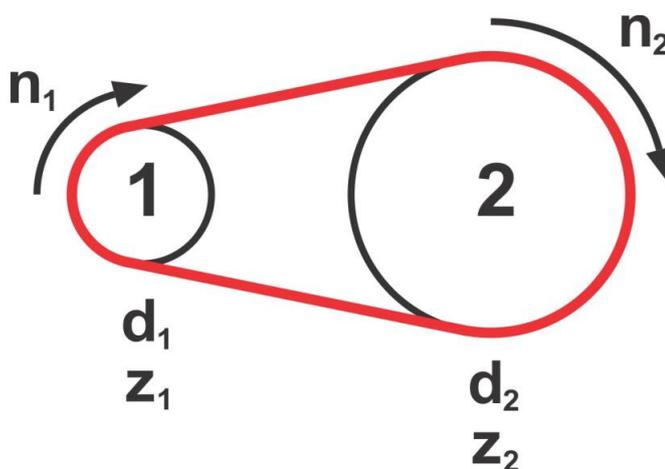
Representação da relação de transmissão de movimento rotativo do eixo motor “1” para o eixo movido “2”
